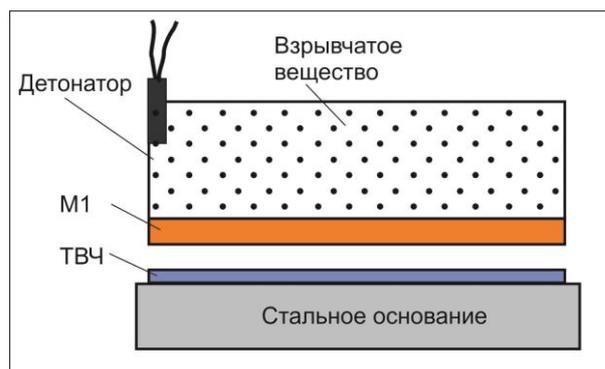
Схема сварки взрывом двухслойного композита "медь – тантал"
